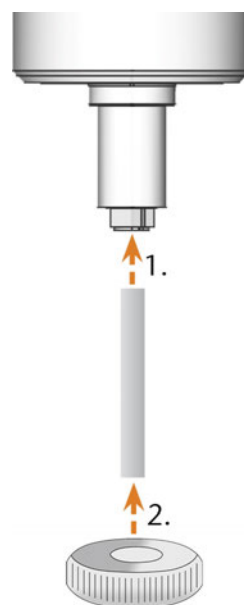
DÉMONTER LA PINCE DE SERRAGE
